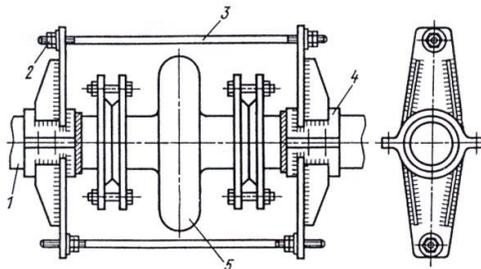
Приспособление для растяжки (сжатия) линзовых компенсаторов:
